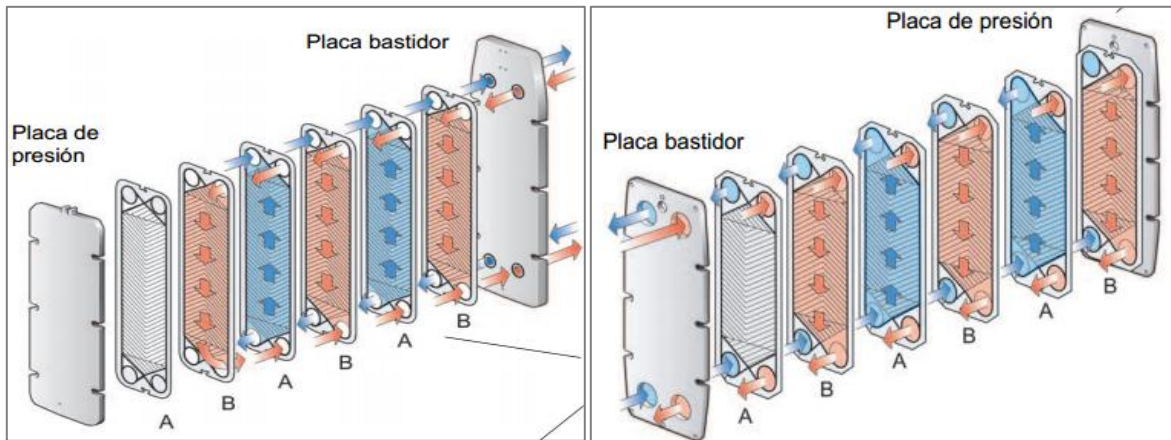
Explosionado del intercambiador de calor de placas planas
